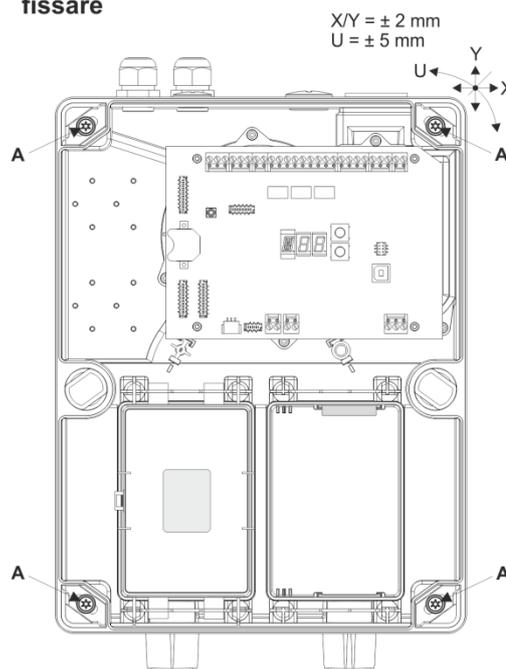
Apertura, chiusura e fissaggio della cassetta rivelatore
